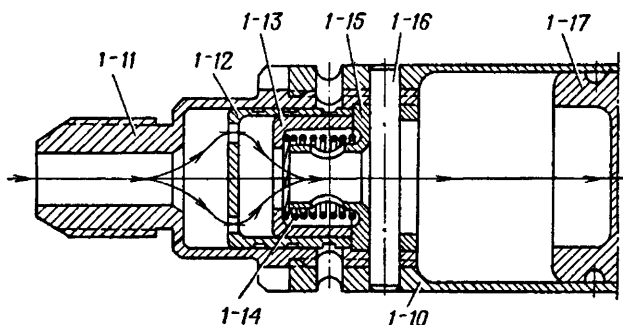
Положение деталей агрегата пневмозарядки при поступлении воздуха в цилиндр пневмоперезарядки (обозначения деталей см. в приложении 1)
